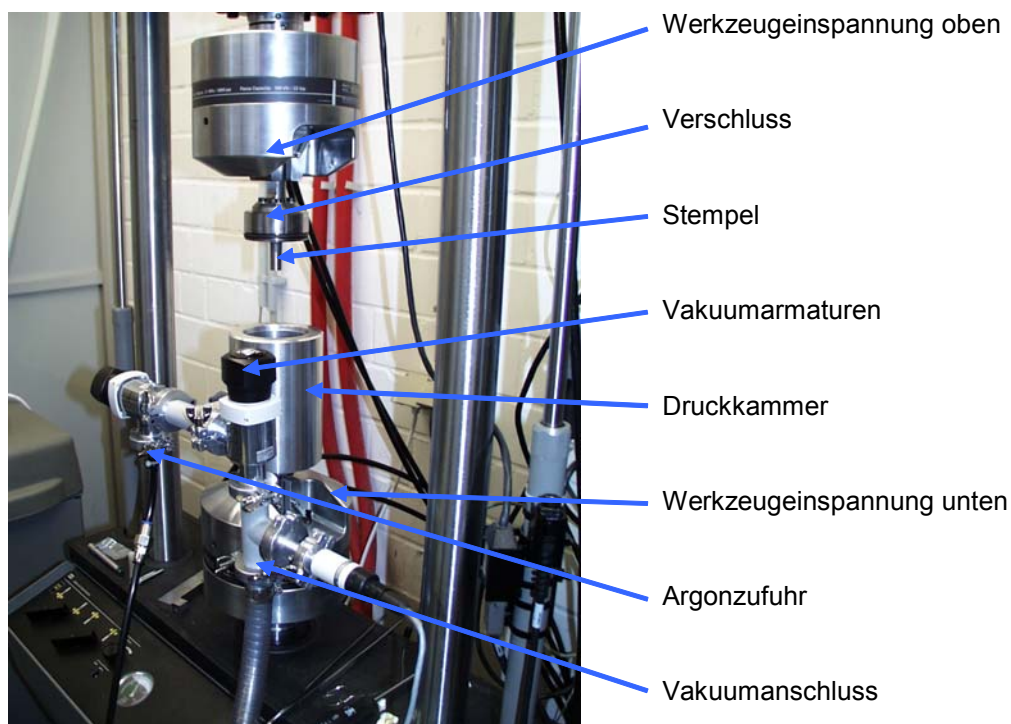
Universalprüfsystem mit Presswerkzeug
